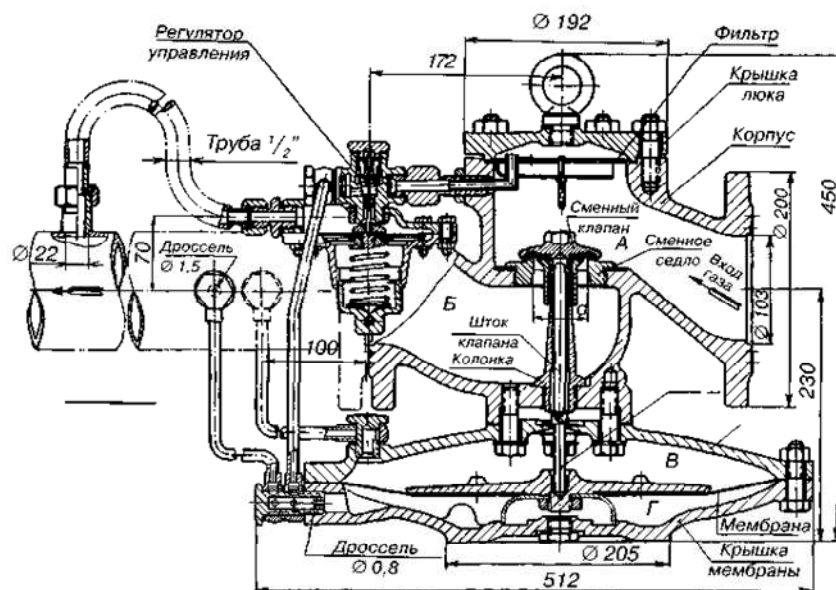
Продольный разрез и схема присоединения регулятора РДУК2-100
